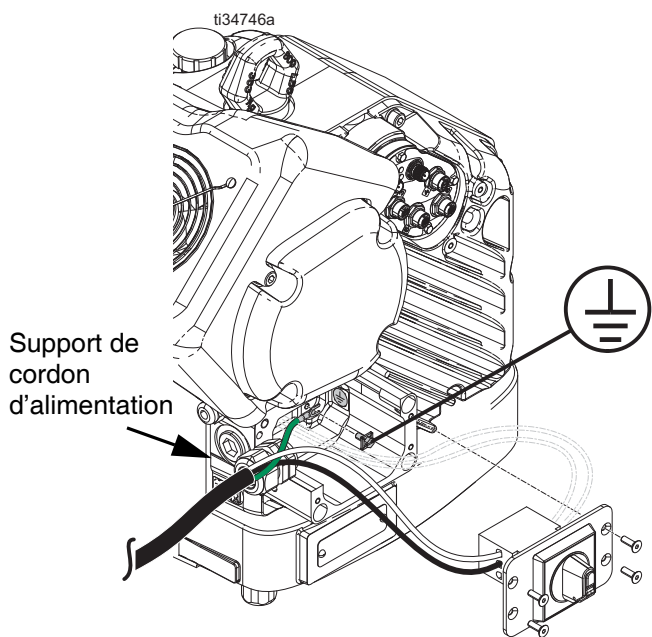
Dépose du couvercle du boîtier de raccordement
